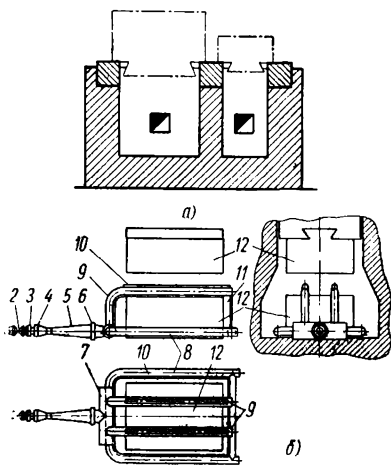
Способы нагрева штампов перед началом работы [13]: а — в печи; б — газовой горелкой непосредственно на молоте; 1 — соединительный штуцер; 2 — кран; 3 — воздушная заслонка; 4 — сопло; 5 — корпус инжекторного смесителя; 6 — соединительная муфта; 7 — коллектор; 8 — боковые патрубки; 9 — верхние патрубки; 10 — планки металлические; 11 — подкладки; 12 — штамп
